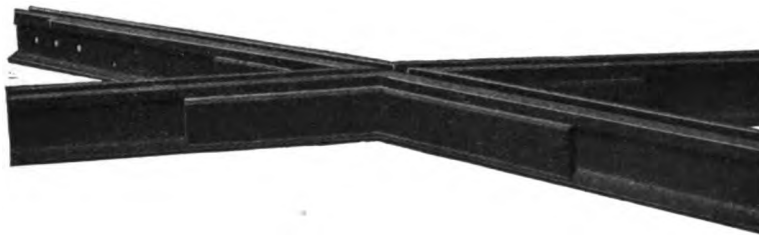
Seitenansicht eines verschweißten Herzstückes, bei dem jede Verschraubung fehlt. Die Seitenlaschen sind starke Flacheisen, die an Kopf und Fuß durch eine nahtförmige Längsschweißung mit den Schienen verbunden sind.
